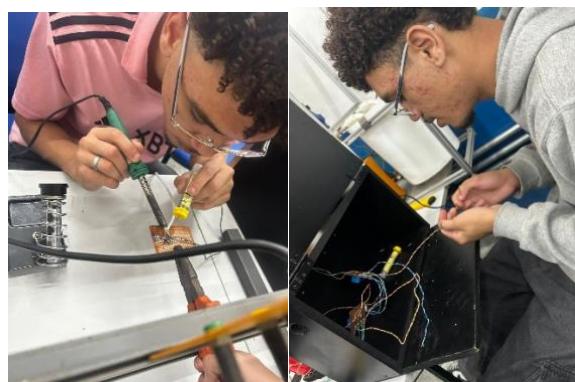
Soldagem na placa de cobre. Fonte Própria
